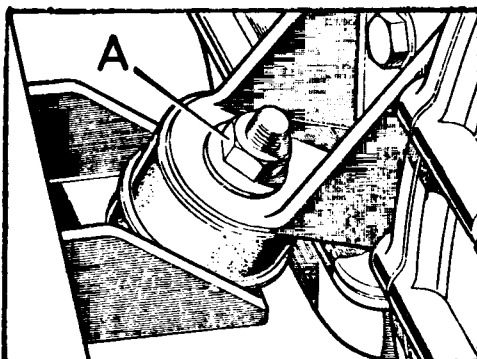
Desmontaje de las tuercas que fijan el motor a sus tacos de apoyo
